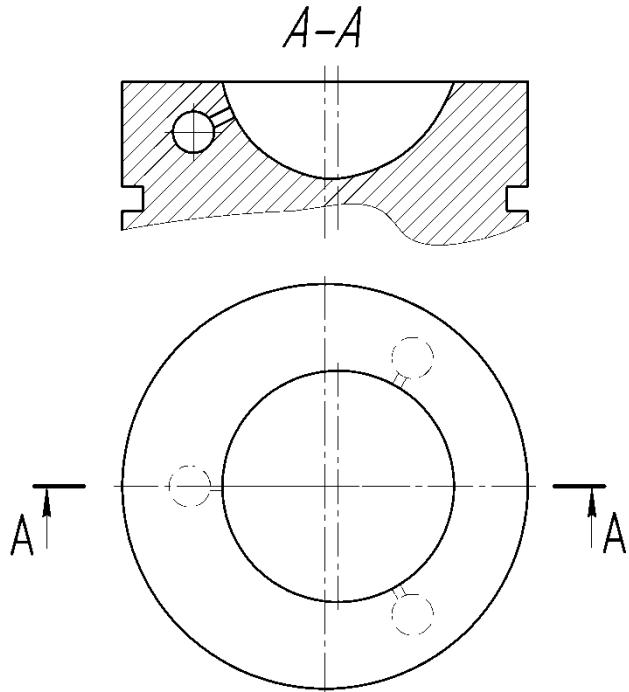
Схема КС с дополнительными камерами в поршне
